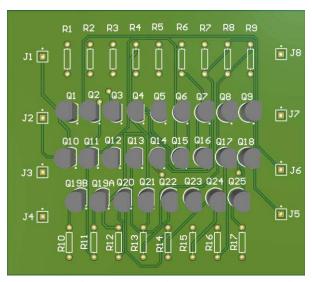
绘图任务二 555 芯片内部电路 PCB 图 3D 效果图
